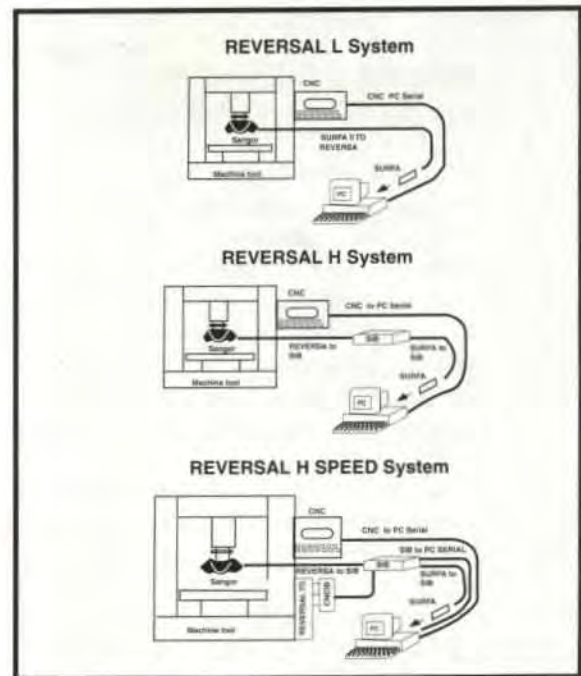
Cabezal láser montado en una máquina herramienta C.N.C.
